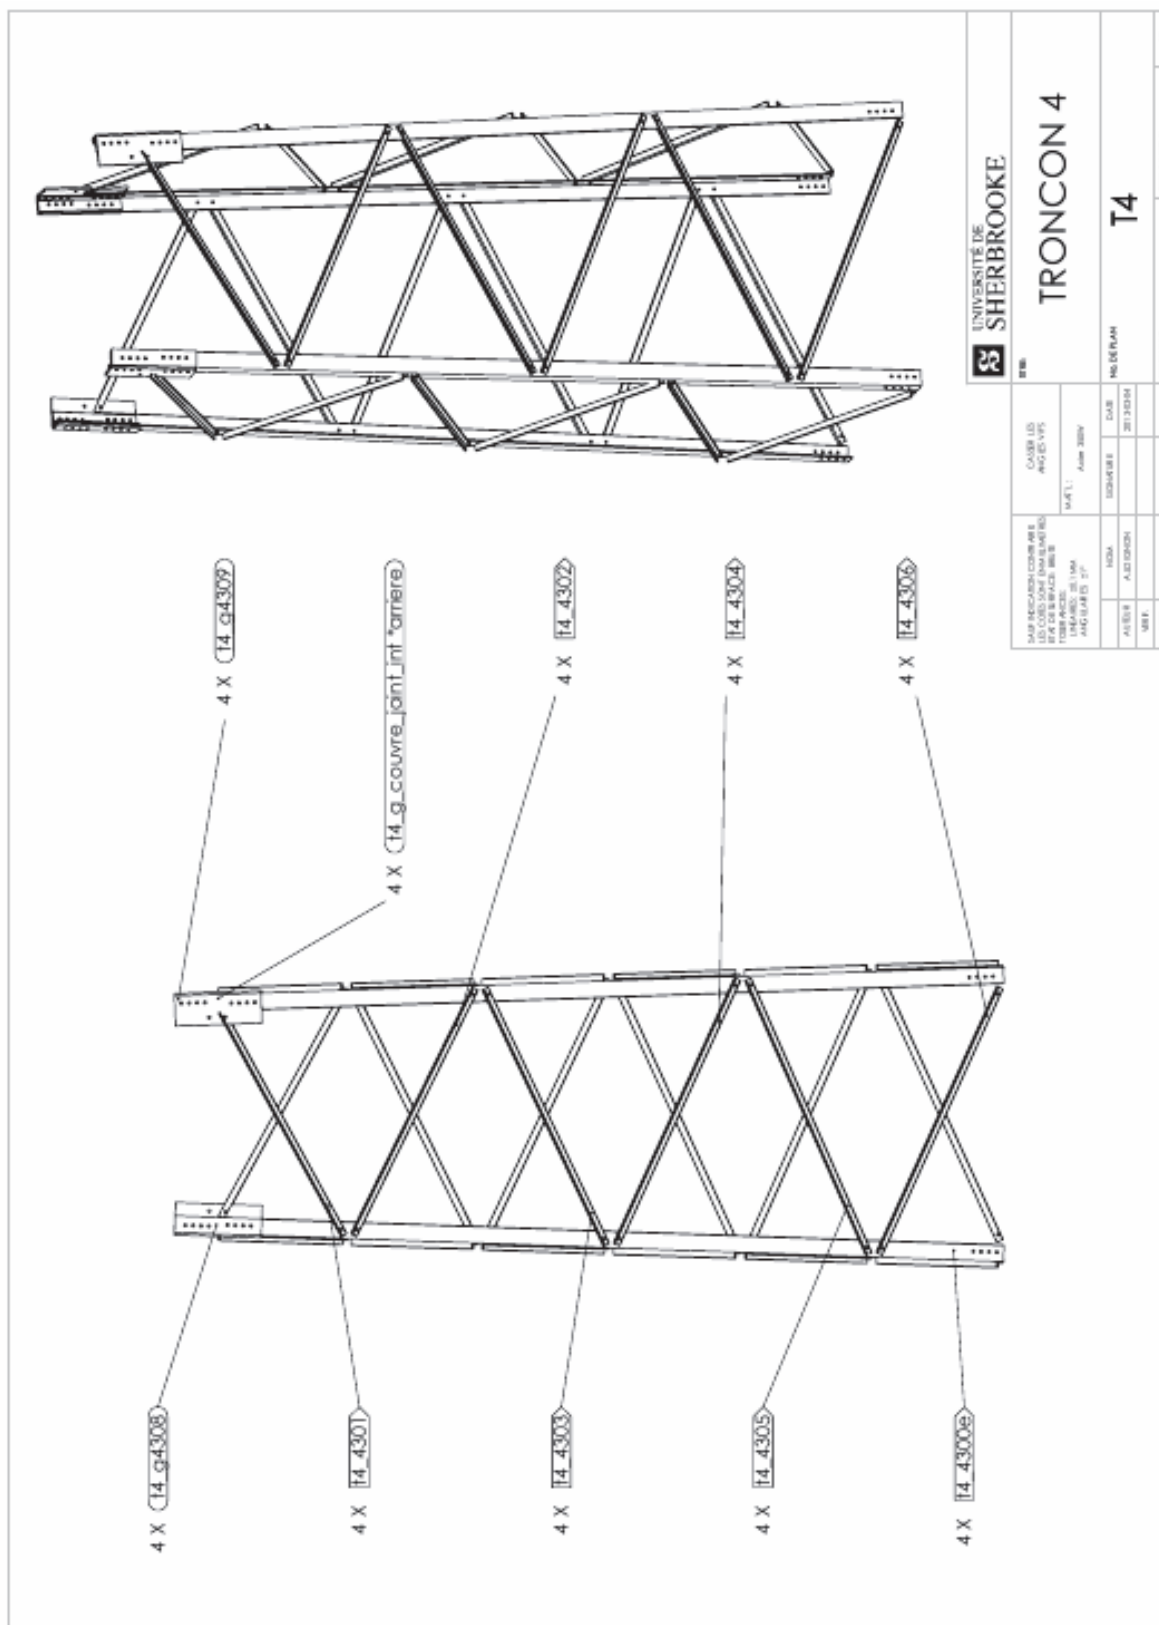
Plan d'assemblage de la sous-structure de fût 34 présenté dans Loignon, A *et coll.* [21]
